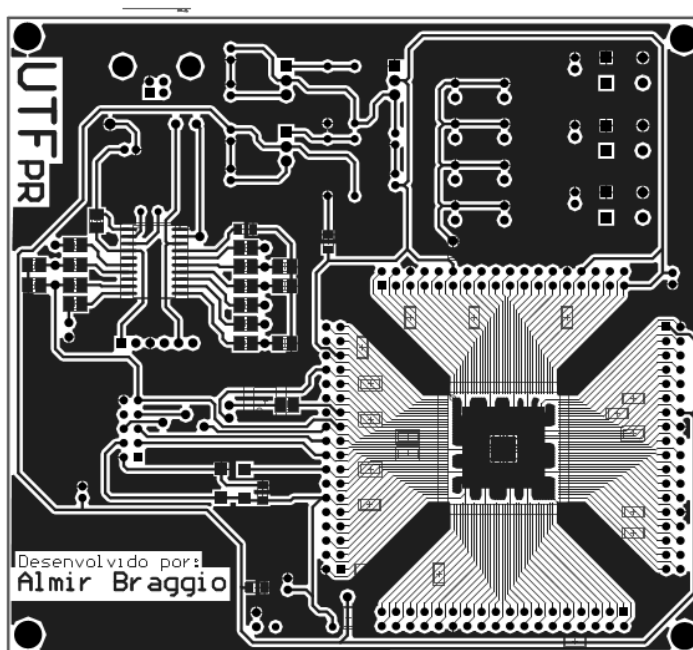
Vista Superior PCB (camada top) (12.4 cm x 11.35 cm)
